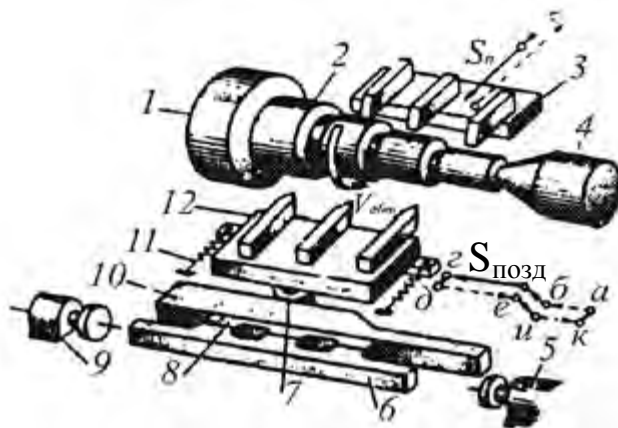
Схема роботи багаторізцевого напівавтомата
